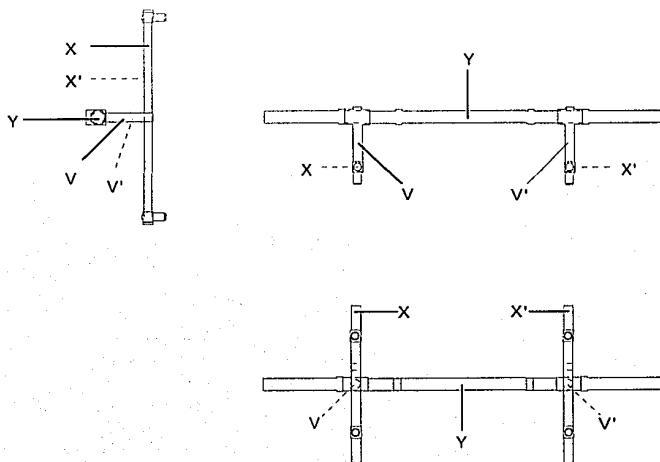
Vistas del sistema mecánico: frontal, de planta y lateral, sistema auxiliar
